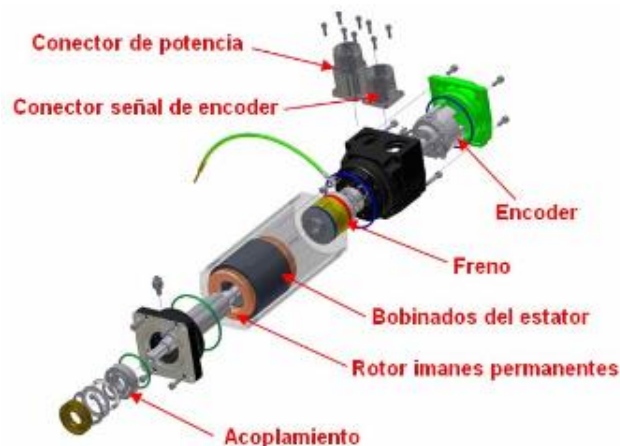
DESPIECE DE LAS PARTES DE UN SERVOMOTOR AC
